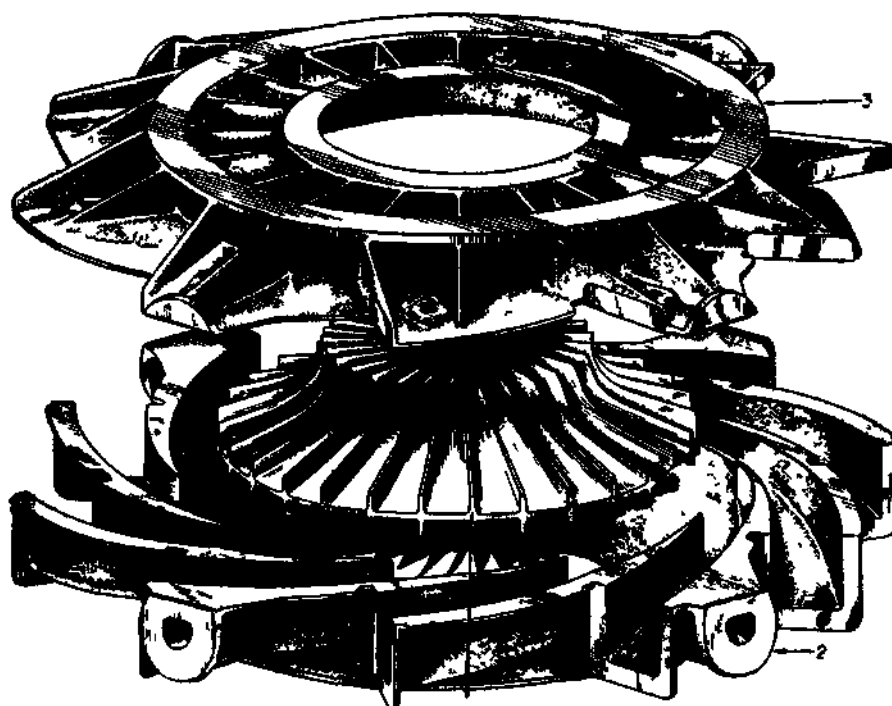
I —Compresor del turborreactor General Electric I-16 1, rotor, 2, difusor y cárter inferior, 3, cárter superior.
